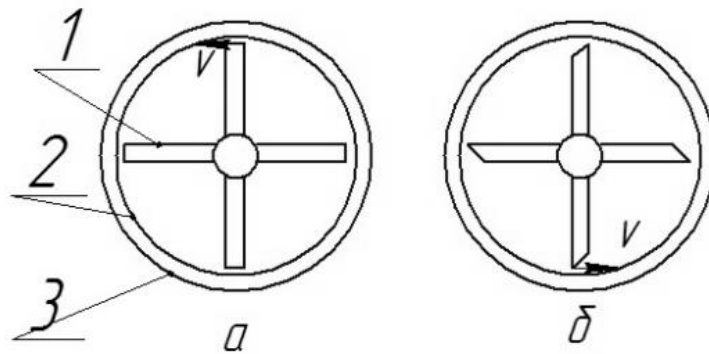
Роторно-плівкові випарні апарати жорсткозакріпленими лопатями:
